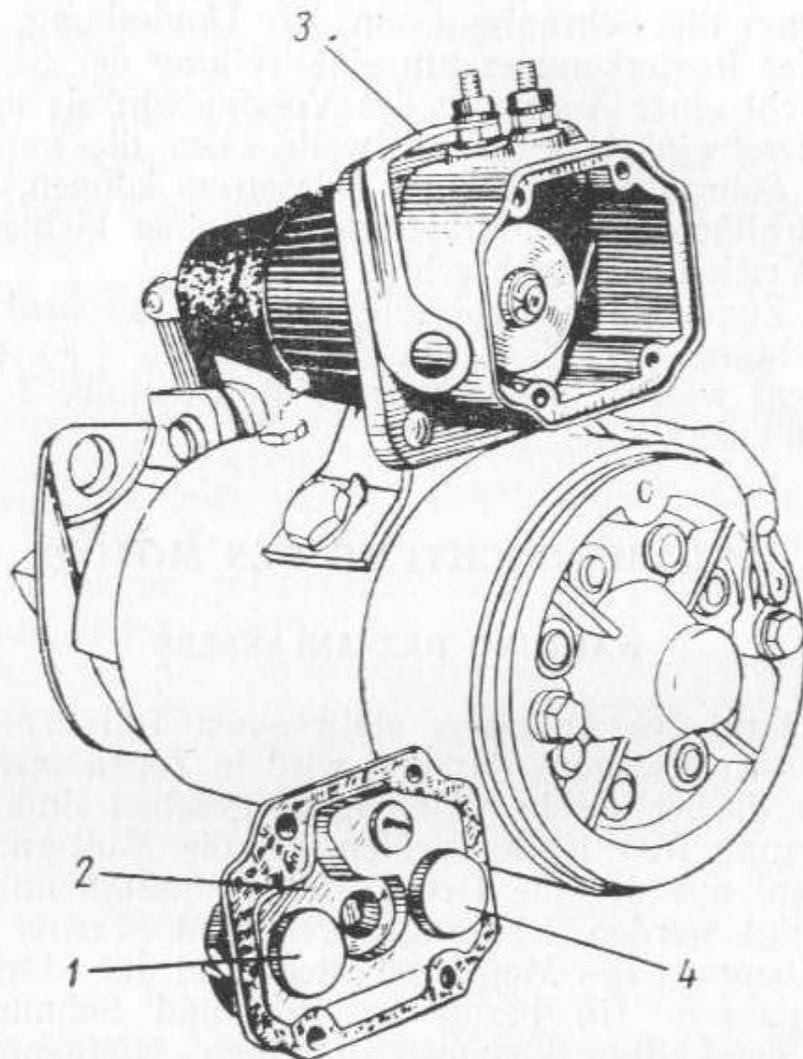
Anlasser Typ CT-4 mit geöffnetem Magnetschalter
